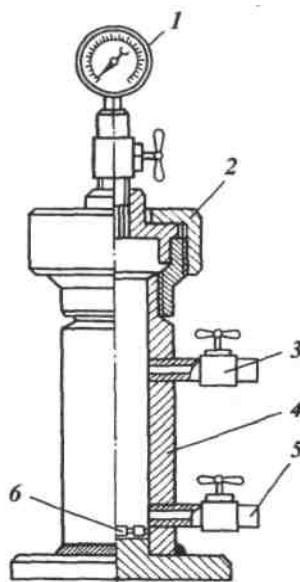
Камера высокого давления: 1 - манометр; 2 - быстросвинчивающаяся гайка; 3, 5 - вентиль; 4 - корпус; 6 - ячейка для установки газлифтного клапана
